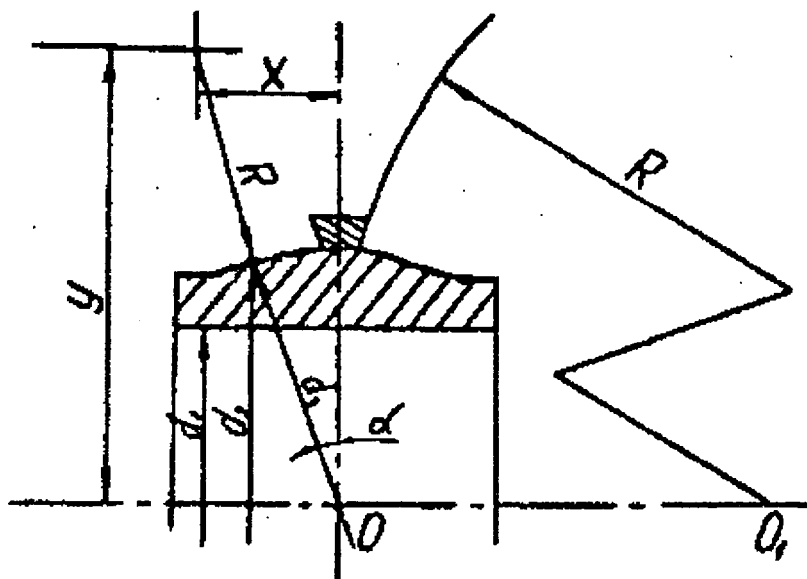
Конструкция внутреннего кольца подшипника с плавающим бортом
